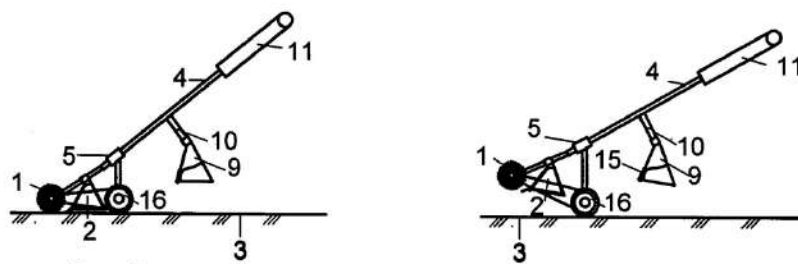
Барабанное устройство для подметания улиц и дорог с прямым приводом: 1–барабанная щетка; 2 – призматический совок; 3– дорога ; 4 – черенок; 5 – патрубок; 6 – ось ОПМ; 7 – колеса; 8 – рама; 9 – компенсирующий призматический совок; 10 – кронштейн; 11 – рукоятка; 12 – винт; 13 – отверстие; 14 – упорный винт; 15 – откидной щиток; 16– двигатель.
